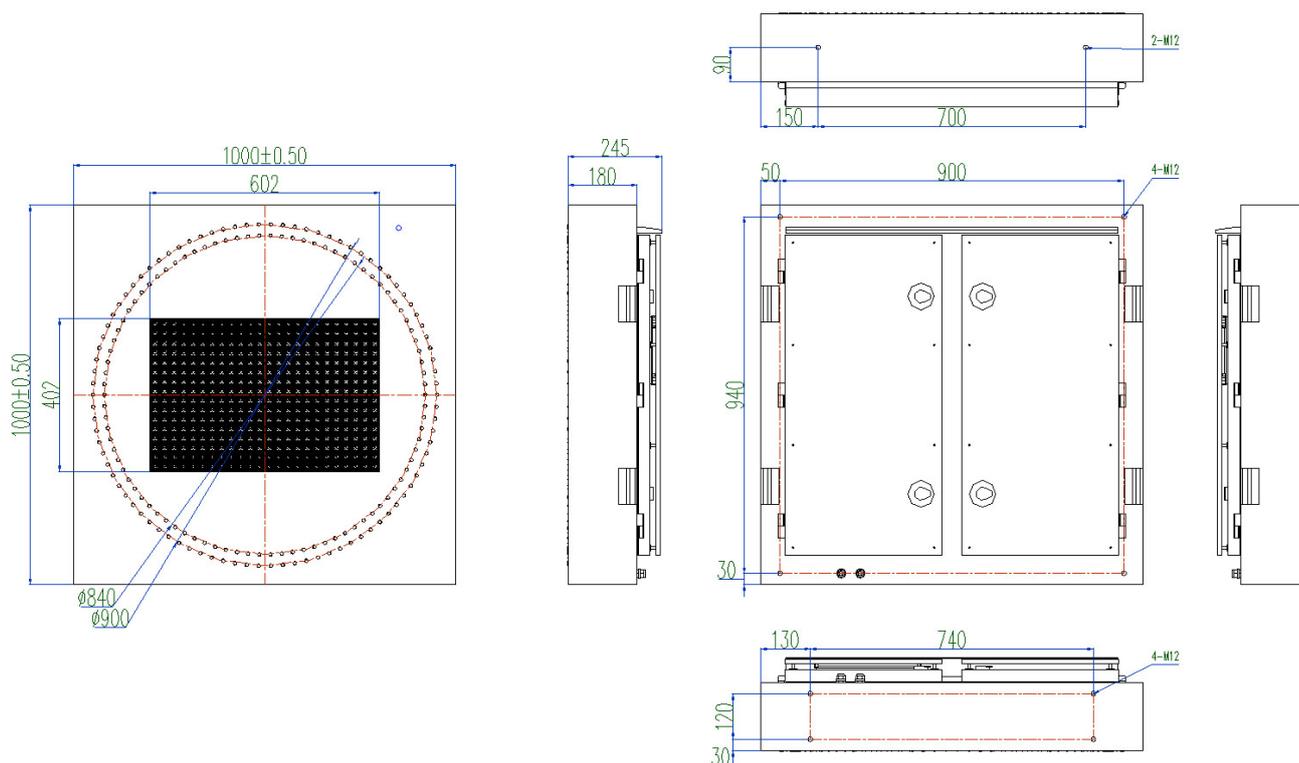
Внешний вид и основные размеры ZOS R25W-090090
